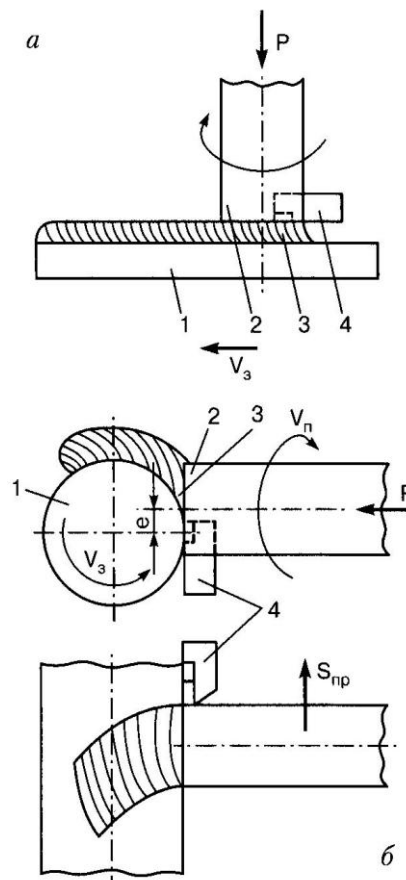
Схема наплавлення тертям витратним інструментом на плоску (а) та циліндричну (б) поверхню
